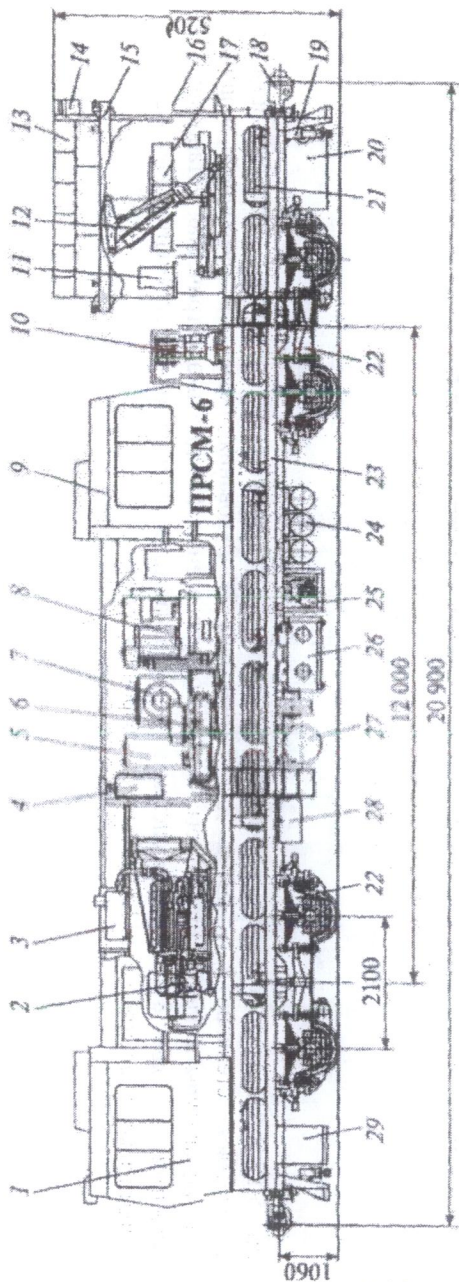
Путевая рельсовсварочная машина ПРСМ-6: 1 и 9 – задняя и передняя кабины управления; 2 и 3 – дизель-электрическая установка и система выхлопа; 4 – расходный бак; 5 – электрооборудование; 6 и 25 – компрессоры; 7 – охлаждающий агрегат; 8 – гидрооборудование; 10 – пресс для испытания пробных сварных стыков; 11 – установка индукционного нагрева рельсов; 12 и 17 – манипулятор и подвесная сварочная машина типа МСР-800.1; 13 и 16 – капот с передней открывающейся торцевой стенкой; 14 – прожектор; 15 – направляющая с электрическими талиями; 18 – автосцепка; 19 – устройство для подтягивания рельсов; 20 – устройство для шлифовки сварных стыков; 21 – роликовый транспортер для пропуска рельсовых плетей; 22 – ходовая тележка; 23 – рама; 24 и 27 – воздушные резервуары тормозной системы и системы охлаждения; 26 – топливный бак; 28 и 29 – ящики: аккумуляторный и инструментальный
